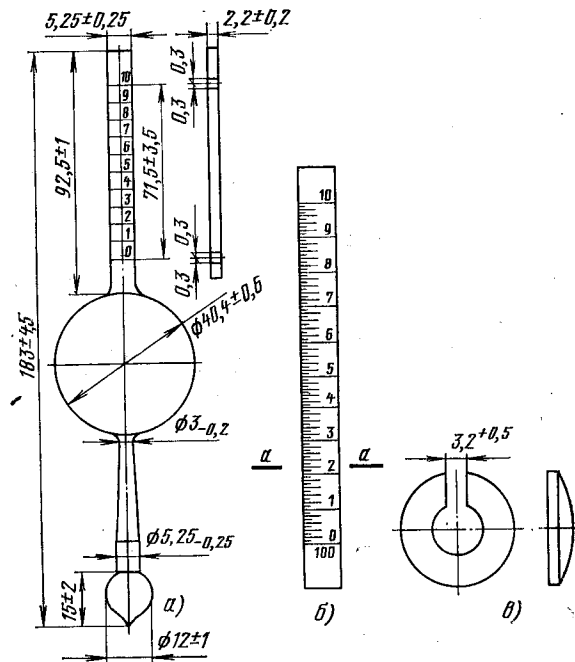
Образцовый 2-го разряда и рабочий металлический спиртомер.
